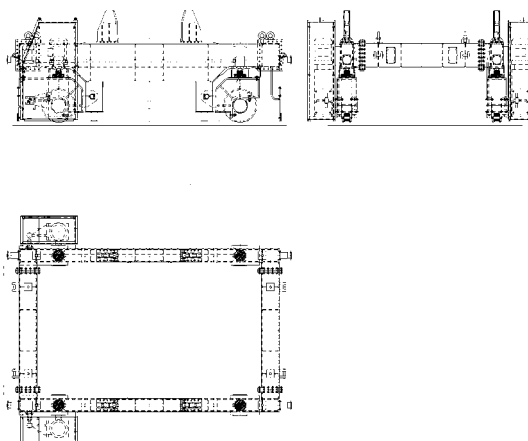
Sistema de pesagem de painelas instalado no carro de vazamento
